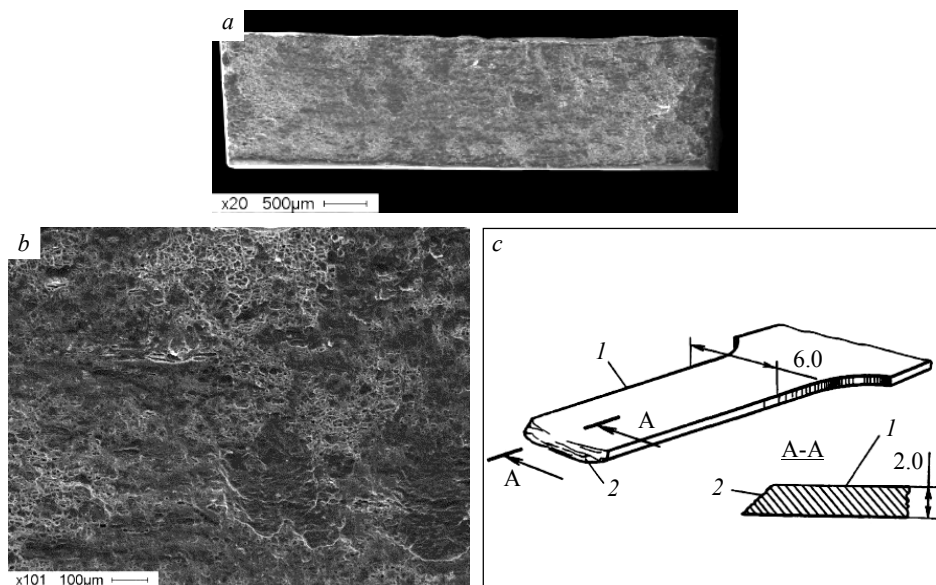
Поверхность излома образца из прокатанного алюминиевого сплава группы 4 без добавления частиц и без обработки УЗ: *a* – общий вид поверхности разрушения, *b* – типичный вид излома; *c* – схема косого излома плоского стального образца, разрушившегося в результате среза при растяжении [27]. В этом случае разрушение произошло вдоль направления действия максимальных касательных напряжений: *1* – образец после испытания на растяжение; *2* – поверхность излома
